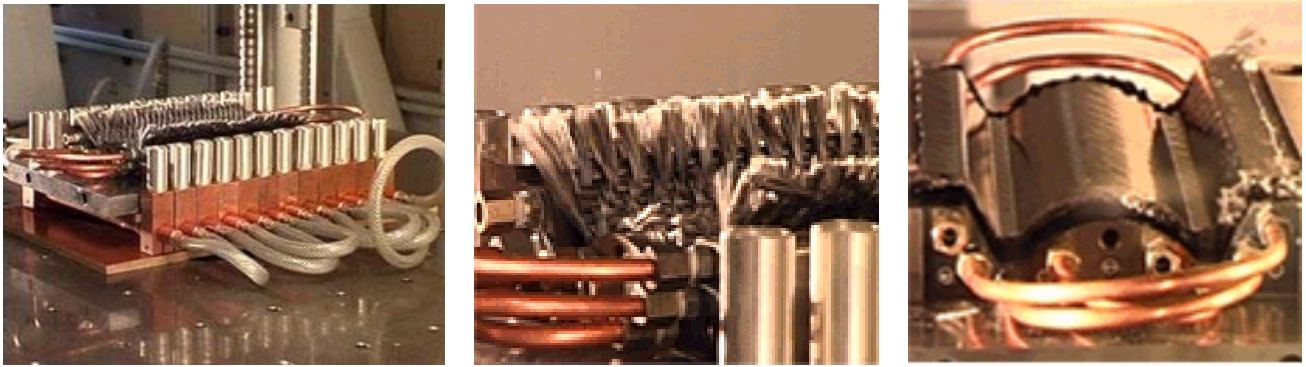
Molde del Cage System ® (mitad inferior) y detalles.
